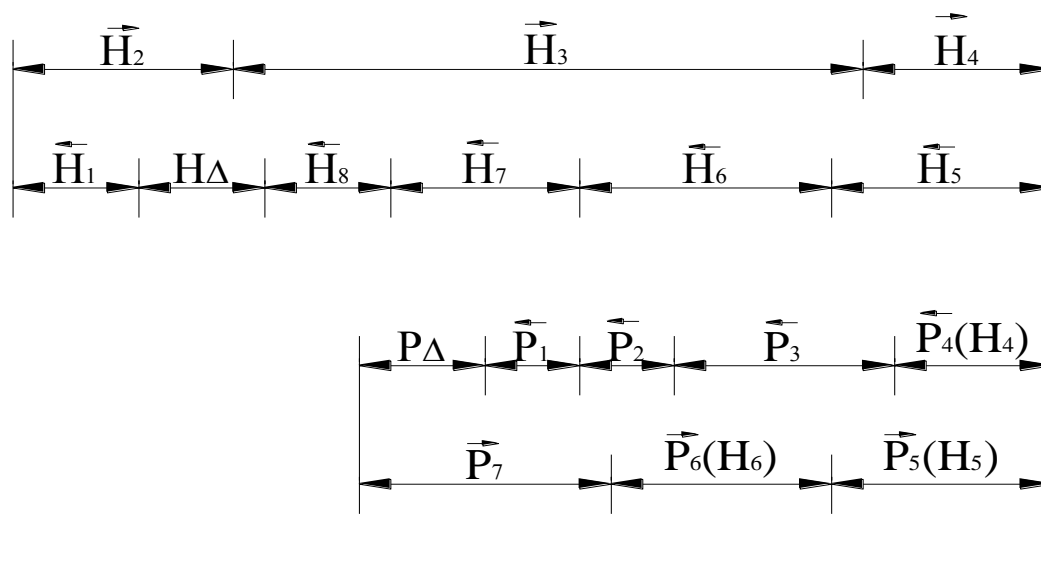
Схемы сборочных размерных цепей вала червячного колеса редуктора
